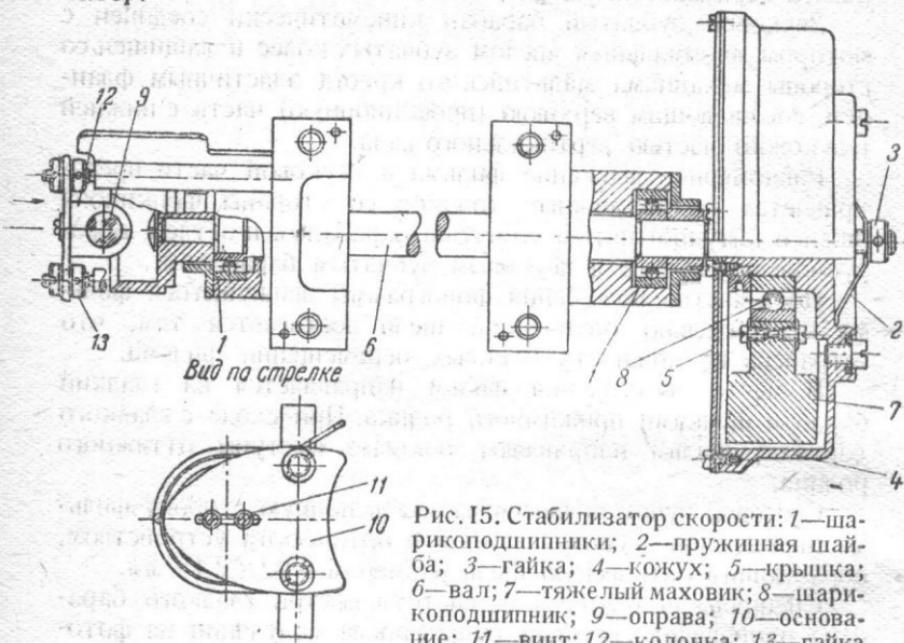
Стабилизатор скорости: 1—шарикоподшипники; 2—пружинная шайба; 3—гайка; 4—кожух; 5—крышка; 6—вал; 7—тяжелый маховик; 8—шарикоподшипник; 9—оправа; 10—основание; 11—винт; 12—колонка; 13—гайка
